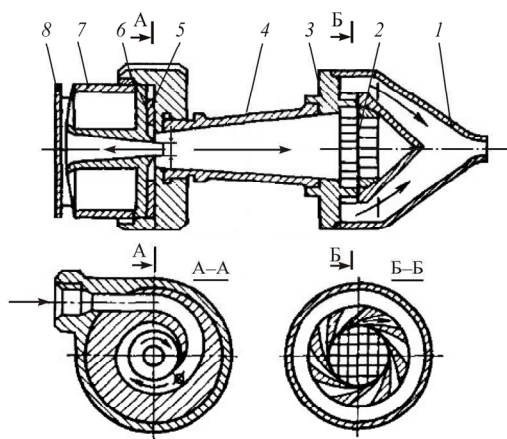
Вихревая трубка Метенина: 1 – патрубок нагретого потока; 2 – сетка; 3 – лопаточный диффузор; 4 – вихревая камера; 5 – сопло; 6 – диафрагма; 7 – патрубок охлажденного потока; 8 – диск
